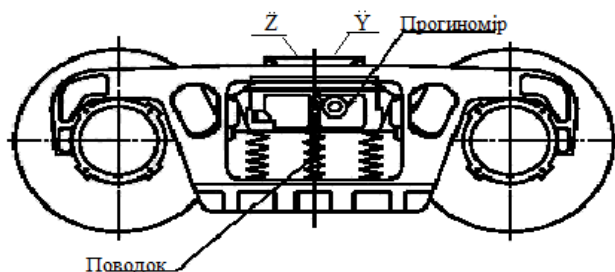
Установка прогиноміра та акселерометрів для вимірювання вертикальних прогинів ресорного підвішування і прискорень обресорених частин візка вагона
